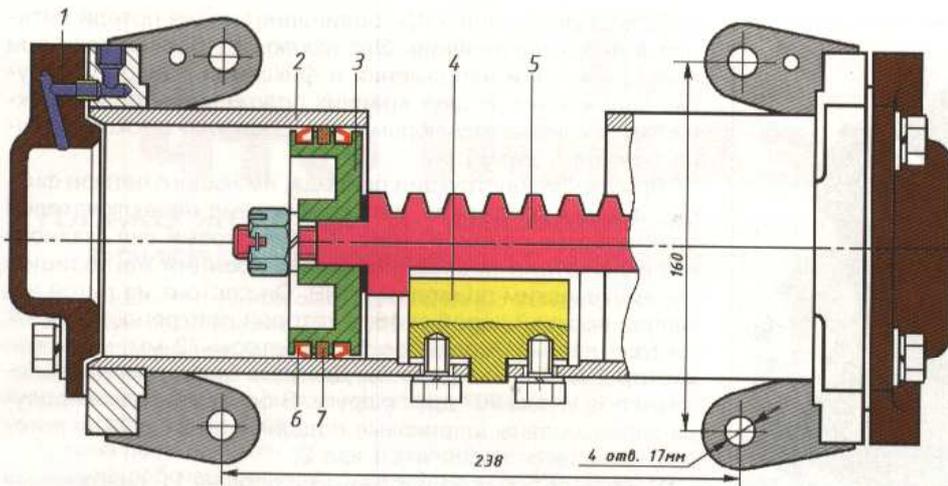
Двухпозиционный привод переключателя ПКГ-040: 1 — крышка цилиндра; 2 — цилиндр; 3 — поршень; 4 — упор; 5 — зубчатая рейка; 6 — резиновые манжеты; 7 — войлочное кольцо
